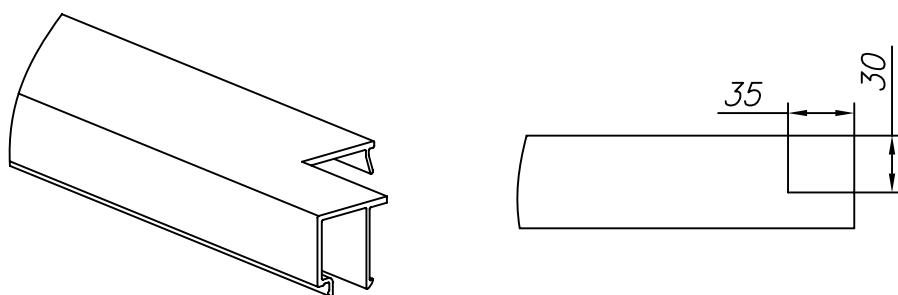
Изготовление паза для тросовой растяжки в профиле штапика FLGU.400.0302, FLGU.400.0304 расположенному вертикально
